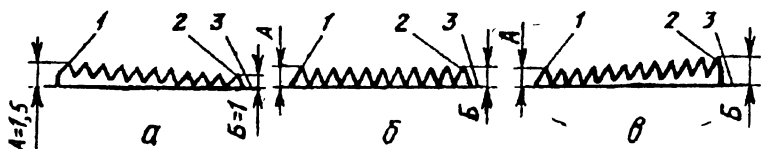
Регулировка высоты зубьев рейки над игольной пластиной (машина 2М кл. ПМЗ):
